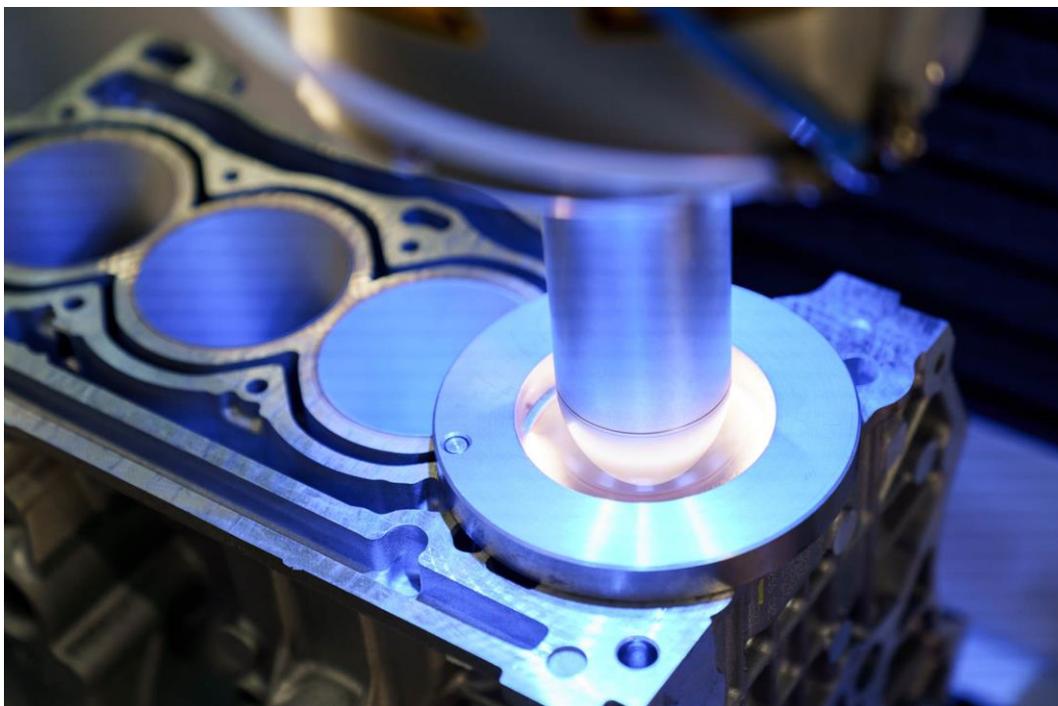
Das Laseraufräumen von Zylinderlaufbahnen ist eine Gearing-Entwicklung, die den Prozess zur Herstellung beschichteter Motoren sicherer und effizienter macht.
